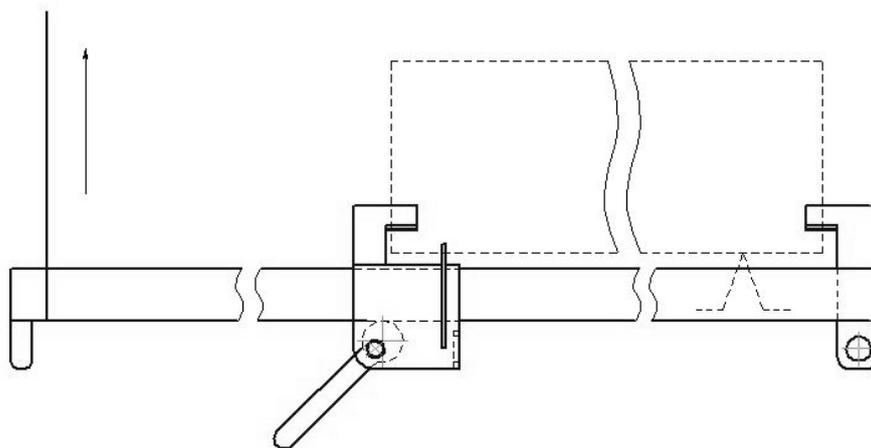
Подъем верхнего края бочки для установки раздающего устройства
